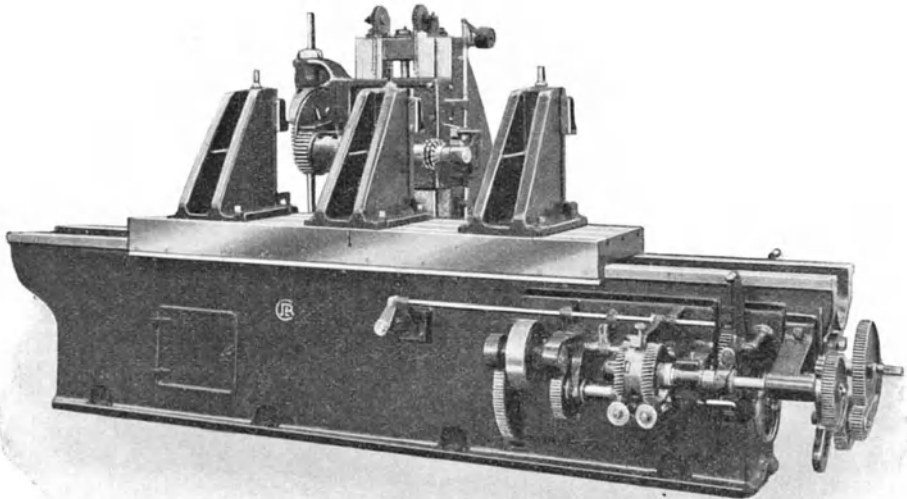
Die Zahnstangenfräsmaschine von J. E. Reinecker.
